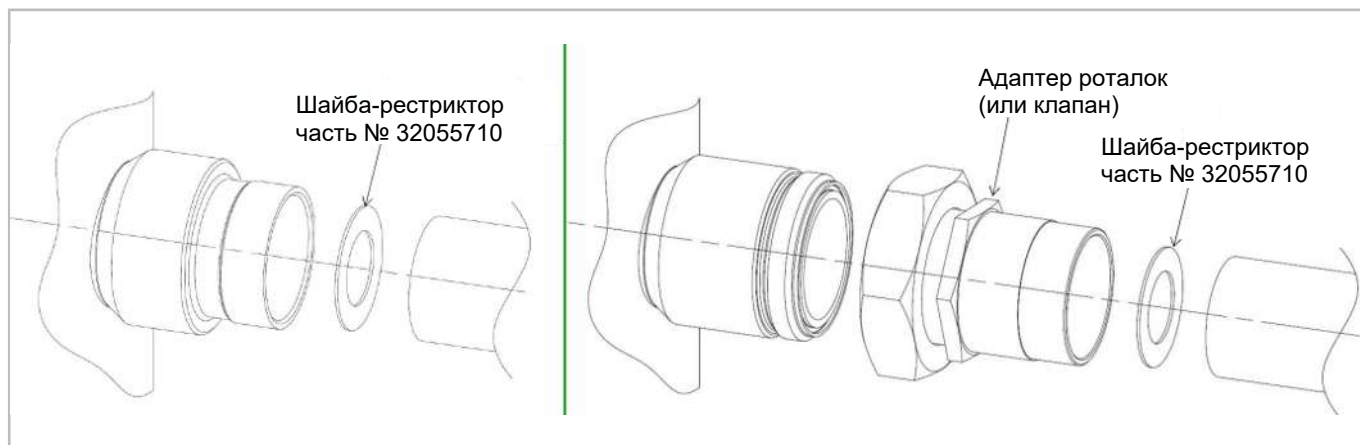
Шайба-рестриктор во всасывающем патрубке в случае использования компрессора GSD80485V.2 в тандеме или трио с компрессорами с обозначением конструкции 1.
